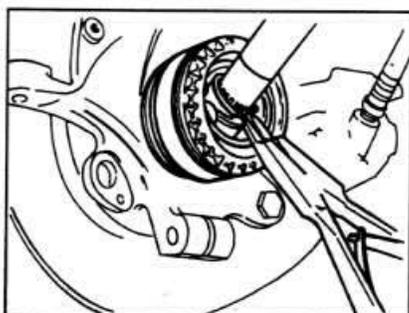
Снятие стопорного кольца крепления наружного шарнира приводного вала.
